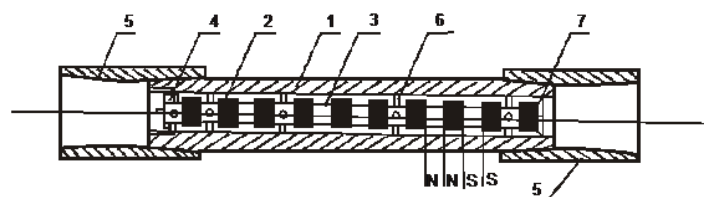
Устьевая магнитная установка: 1 — корпус-патрубок с диаметром 73 мм; 2 — постоянный магнит ЮН14ДК24Т2; 3 — немагнитические разъединяющие втулки; 4 — зажимное кольцо; 5 — муфта соединительная; 6 — центрирующие стержни; 7 — упорное кольцо
